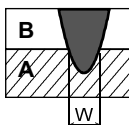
Ansatz zum Schweißen zweier seither nicht miteinander schweißbarer Werkstoffe mit Hilfe der Mehrfokustechnik in Queranordnung.
